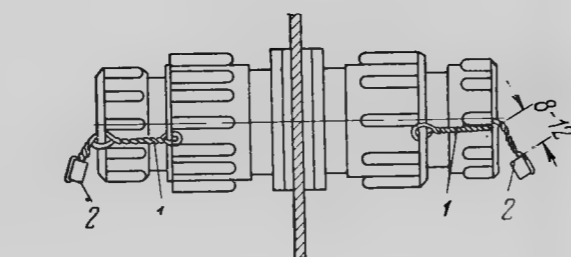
Контровка штепсельных разъемов типа ШРНГ (вид контровки 7):
